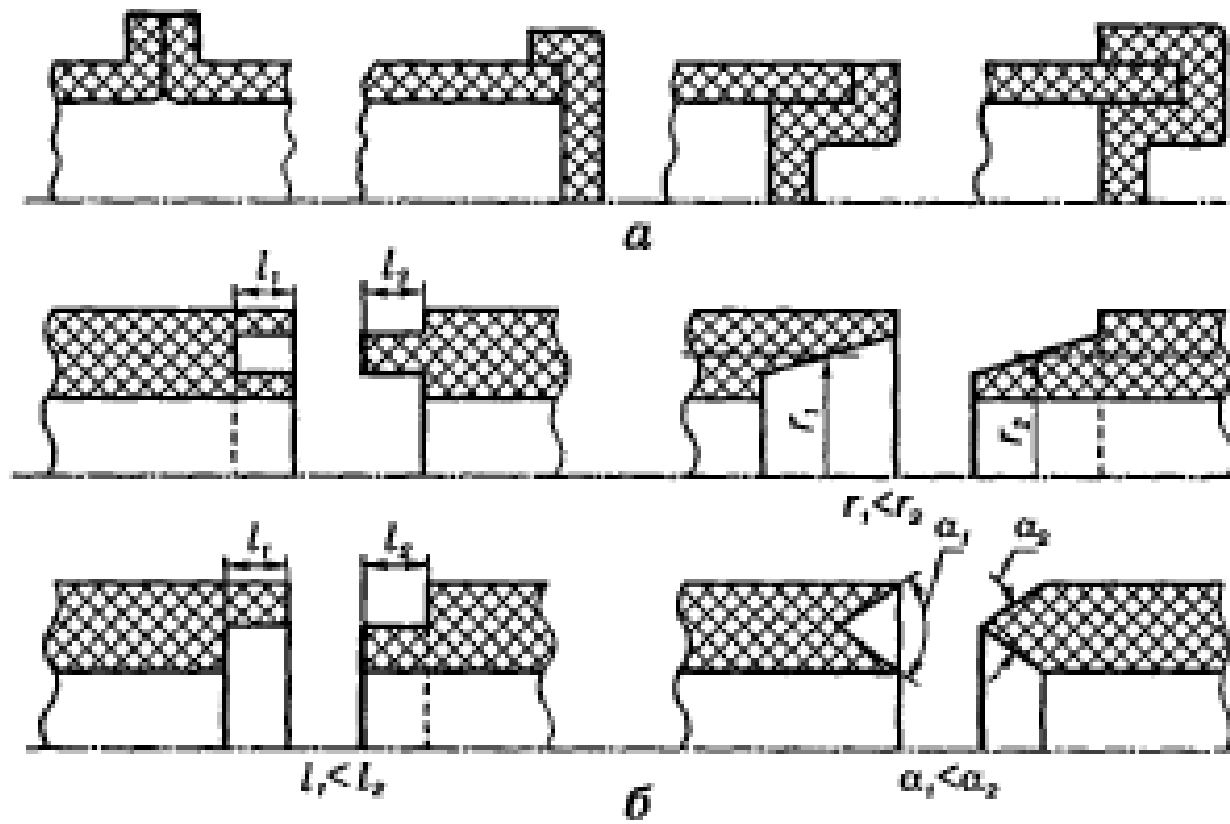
Види з'єднань циліндричних стінок з денцем і обробка кромки труб для зварювання тертям
